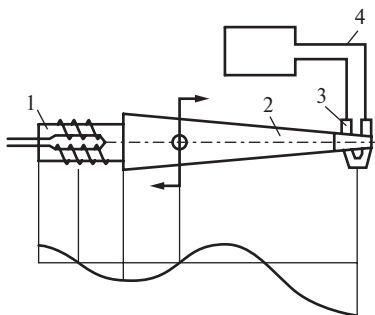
Схема термокомпрессионной сварки с наложением ультразвуковых колебаний
